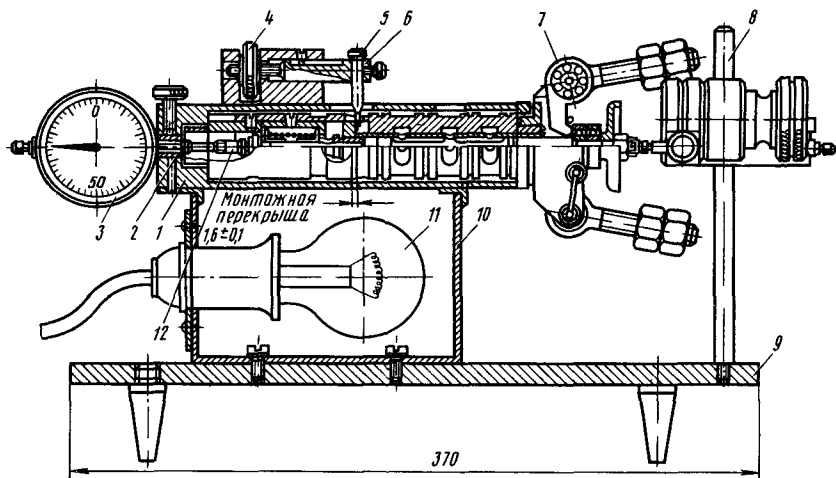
Приспособление для регулировки золотниковой части всережимного регулятора:
